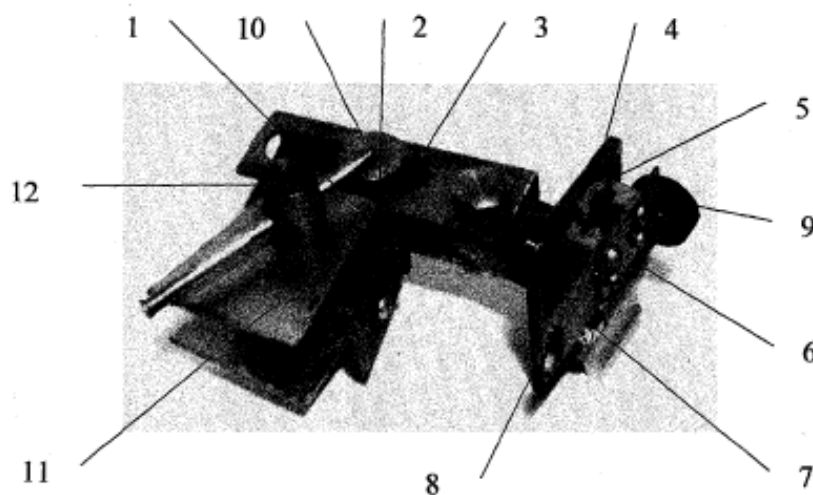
Пристосування для нарізання канавок на зубах:
